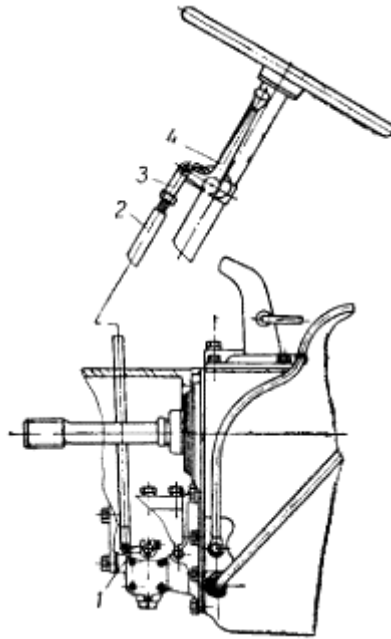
Регулювання приводу перемикання передач коробки передач трактора ХТЗ-17221
